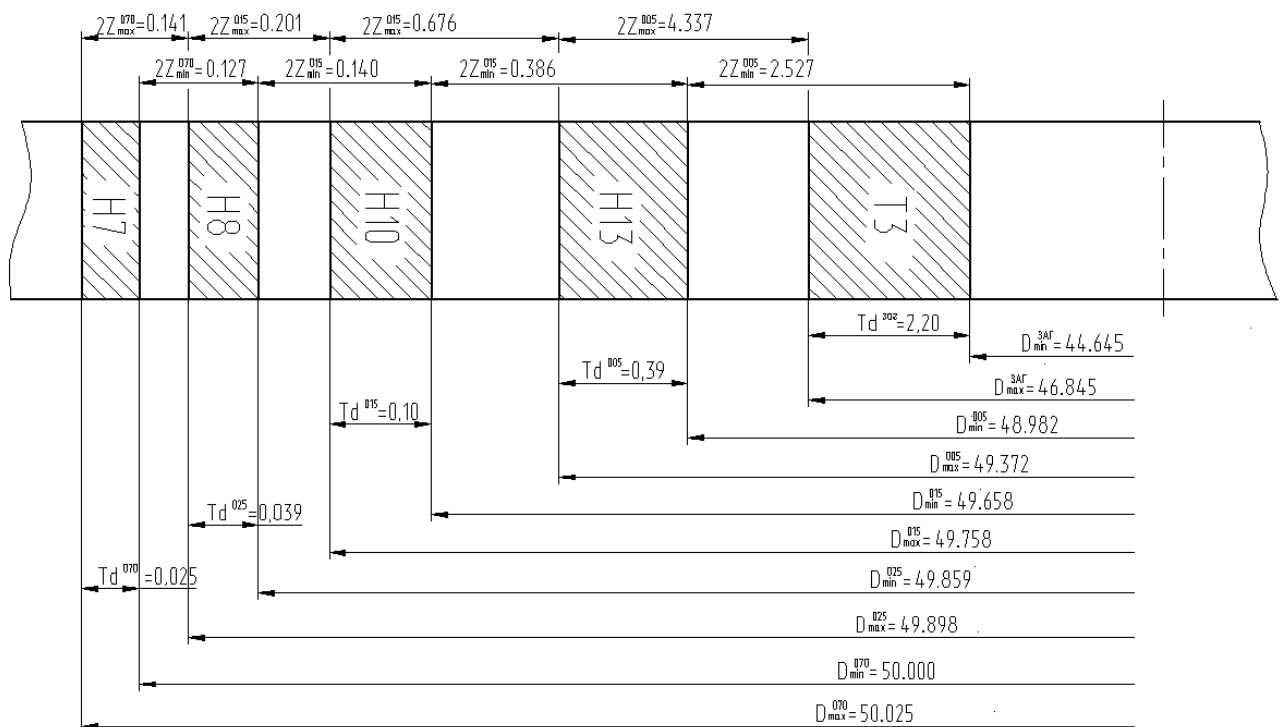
Схематическое изображение расположения припусков, допусков на обработку и размеров на $\varnothing 50H7^{(+0,025)}$
